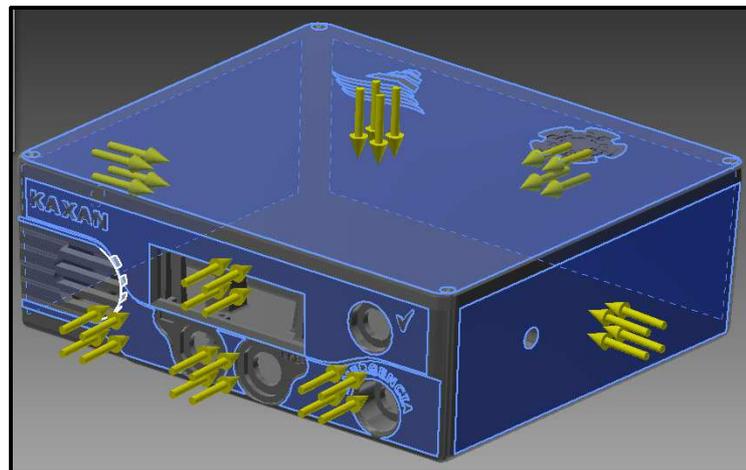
Aplicación de cargas a la geometría del gabinete
